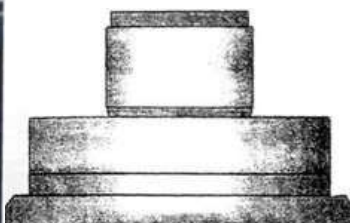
Крышка ковша печи из металлического кожуха с размещенными внутри трубами водяного охлаждения.
